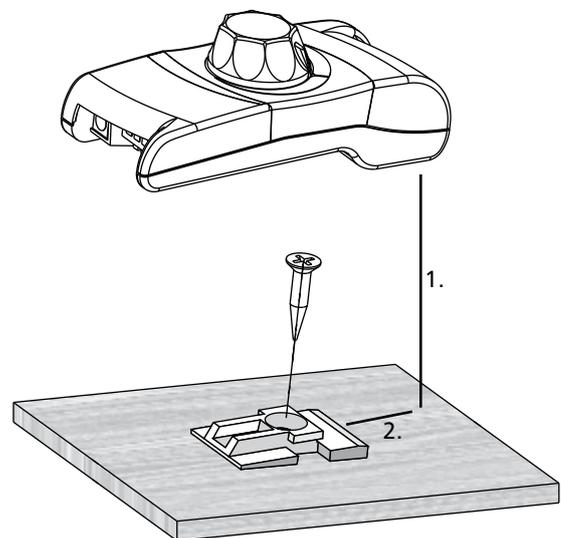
Das Befestigen des Gerätes auf einer Grundplatte
